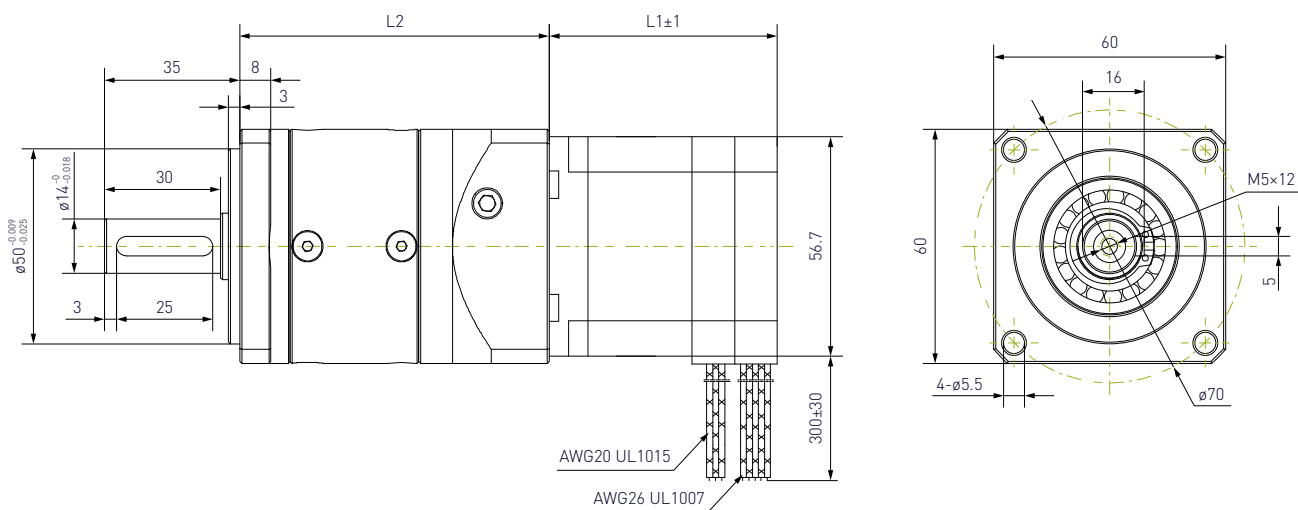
Габаритный чертеж мотор-редуктора.
